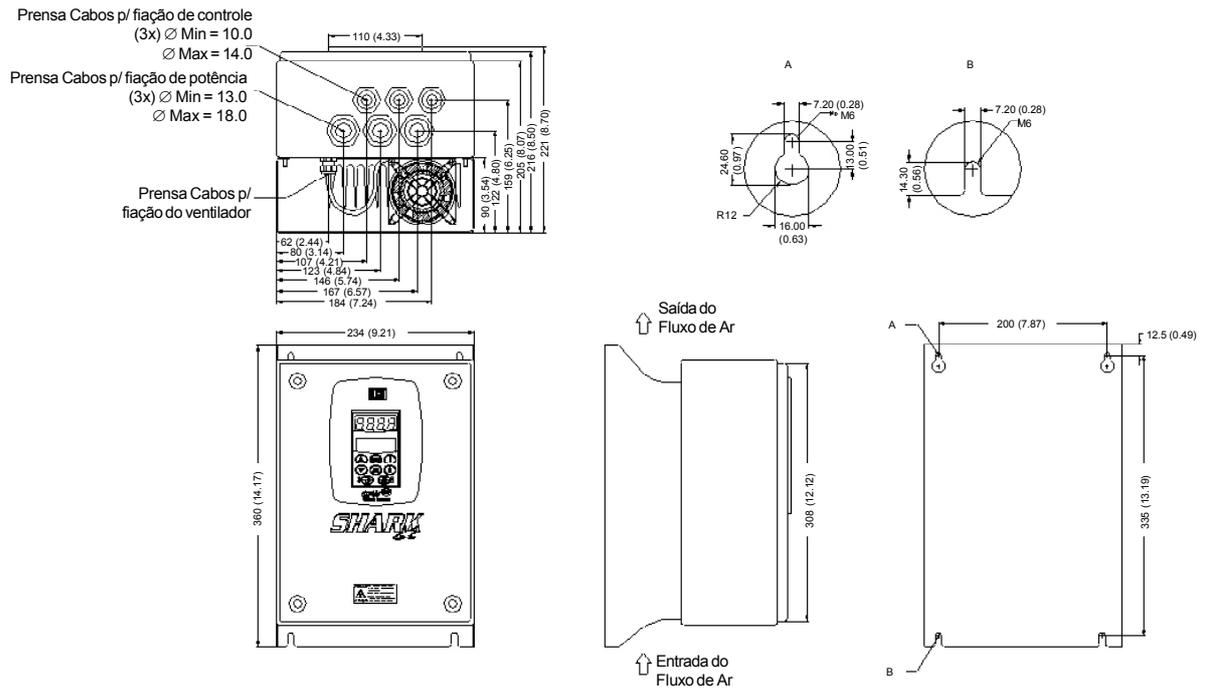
Dados dimensionais em mm (in) - Mecânica 1
